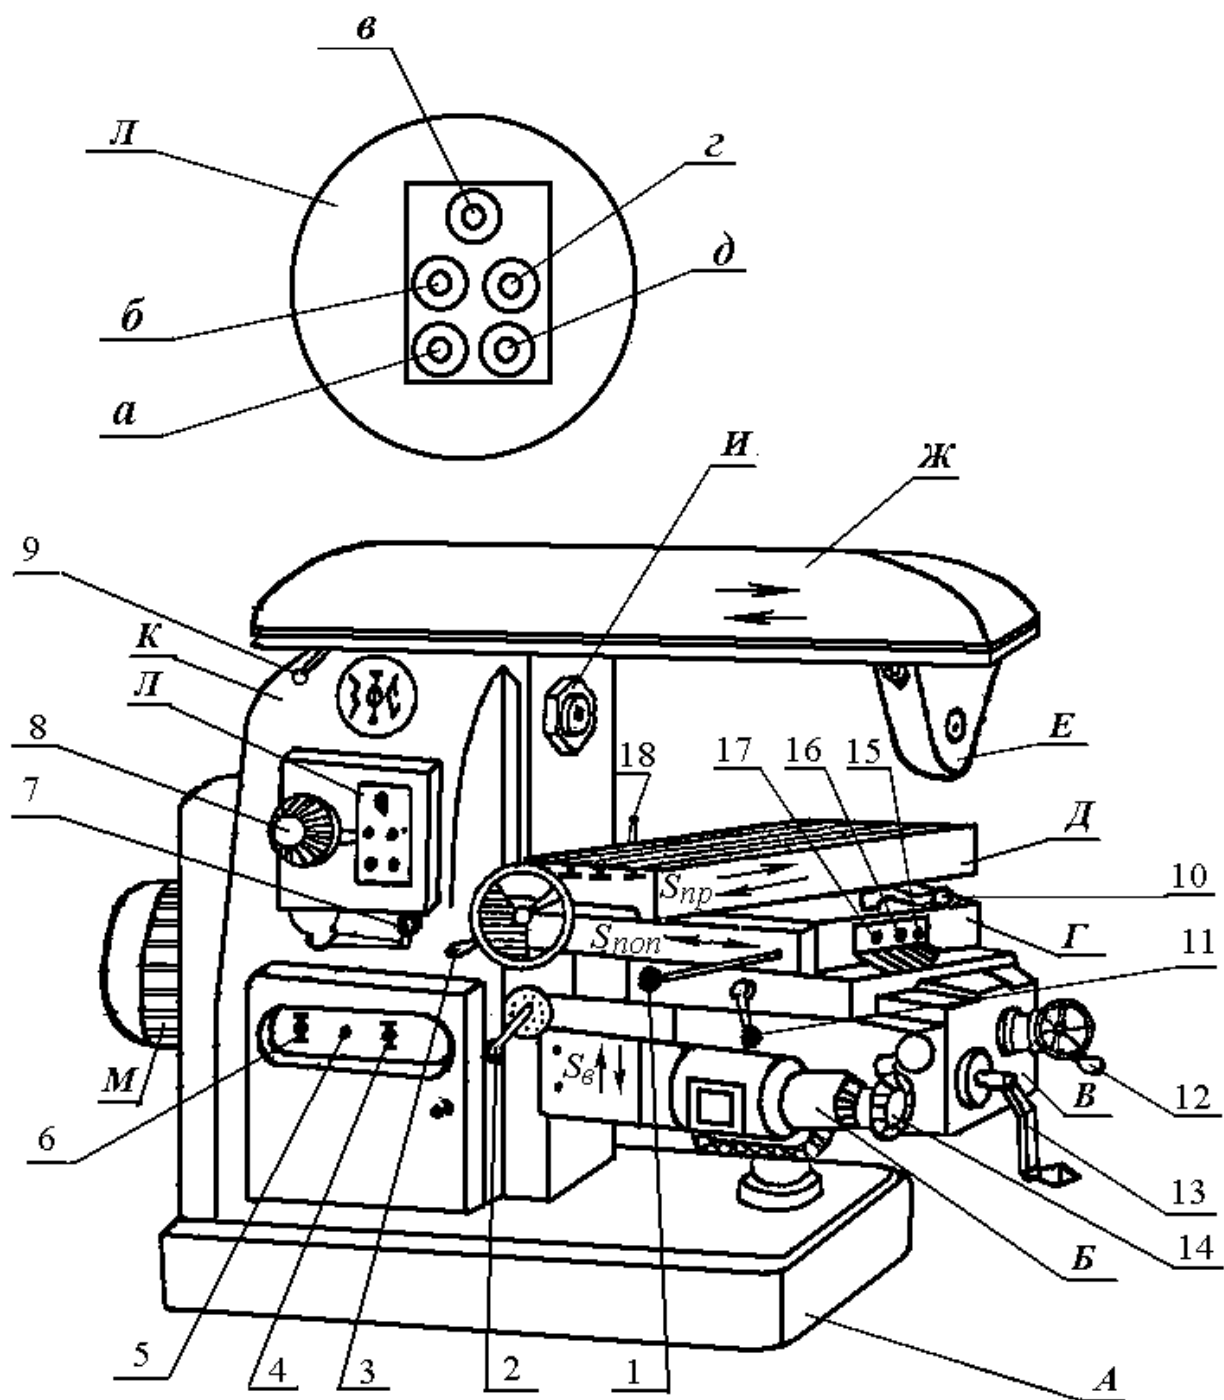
Общий вид горизонтально-фрезерного станка 6М82
